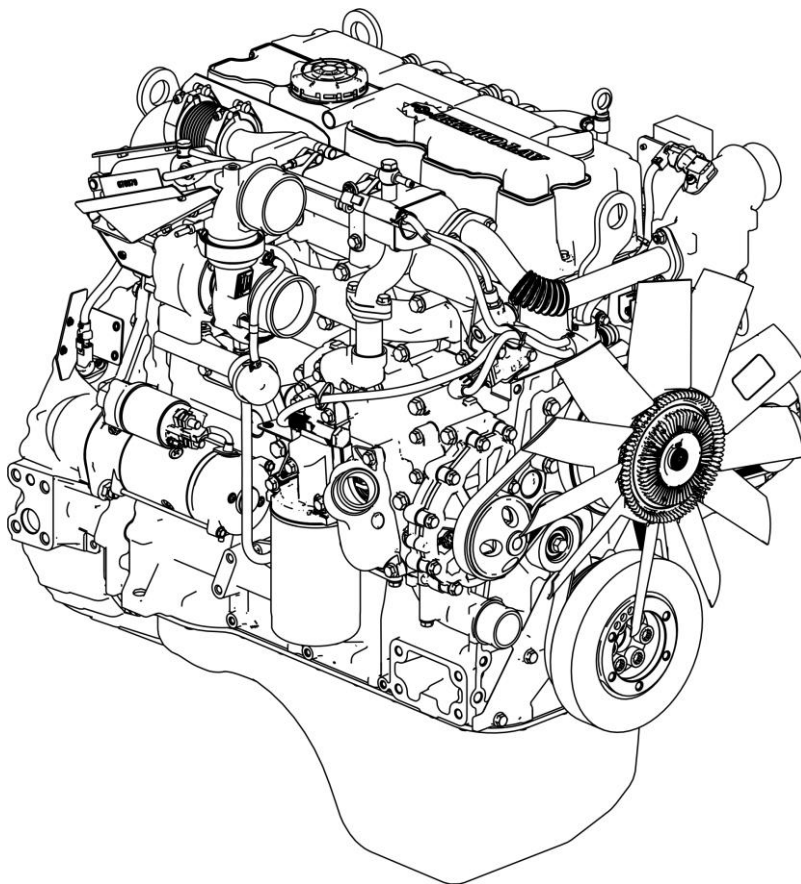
Двигатель ЯМЗ-53443-30 (общий вид справа)
